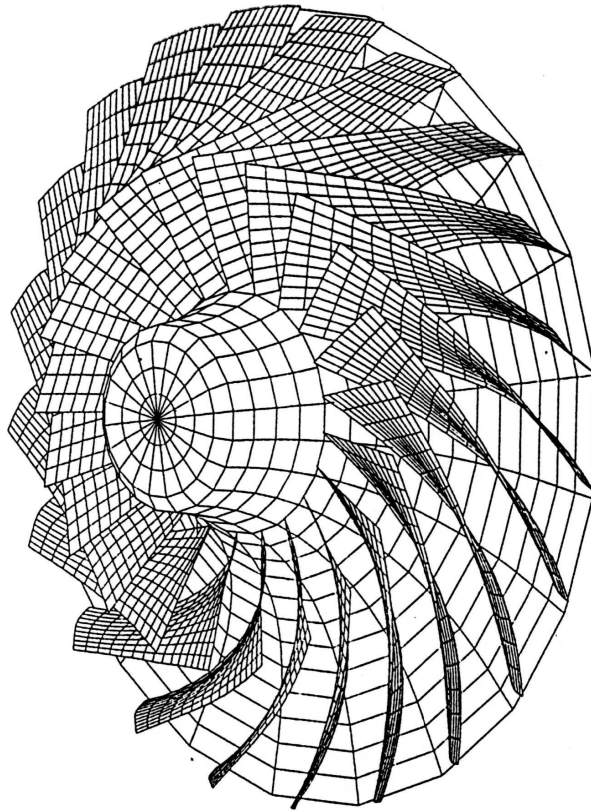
Compresseurs centrifuge et axial – Dessin 3D.
